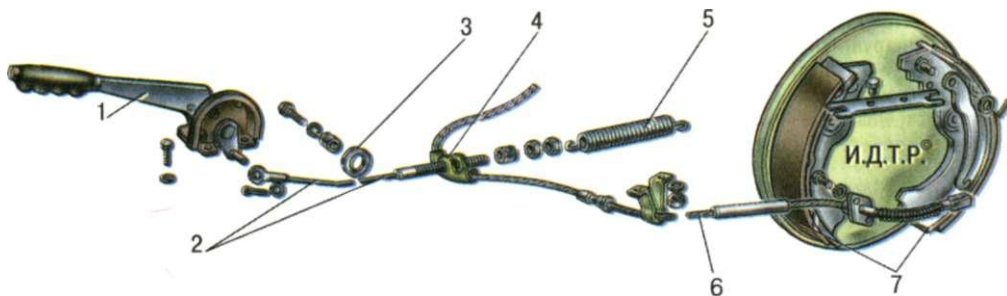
Привод стояночного тормоза: 1 - рычаг с кнопкой привода стояночного тормоза; 2 - передаточный трос; 3 - ролик; 4 - направляющая заднего троса; 5 - оттяжная пружина; 6 - задний трос; 7 - колодки заднего колеса
